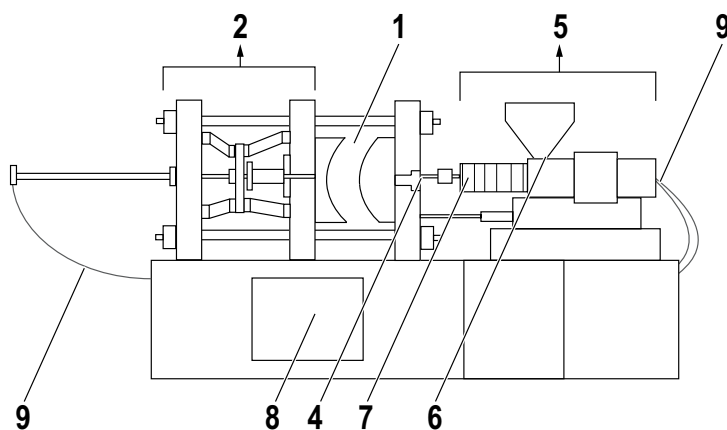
Zones de danger d'une machine de moulage par injection (vue de face)
